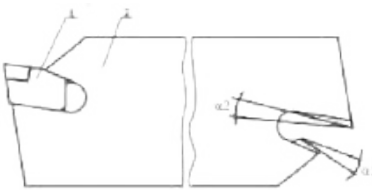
Конструкція збірного відрізного різця для важких токарних верстатів: 1 — різальний клиновий елемент; 2 — корпус
